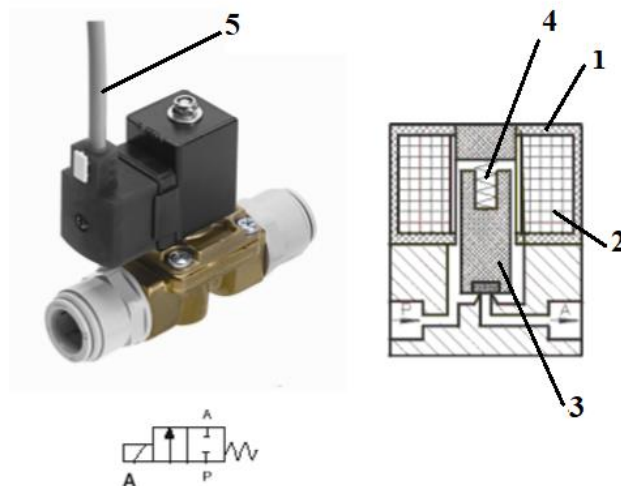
Загальний вигляд та принципова схема електромагнітного клапана: 1 – корпус; 2 – котушка індуктивності; 3 – шток; 4 – пружина; 5 – кабель живлення;
